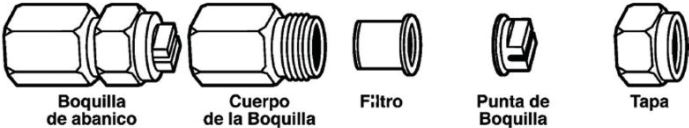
Detalle de partes que componen el cuerpo de una boquilla sin difusor.
